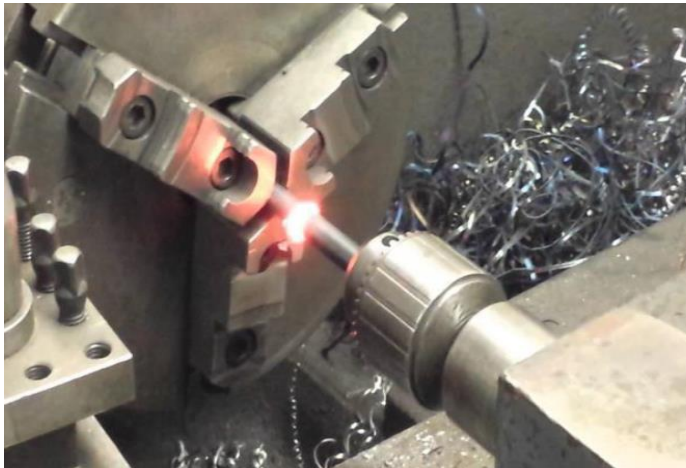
Soldadura por fricción rotativa. Fuente: Nicholas (2003).
